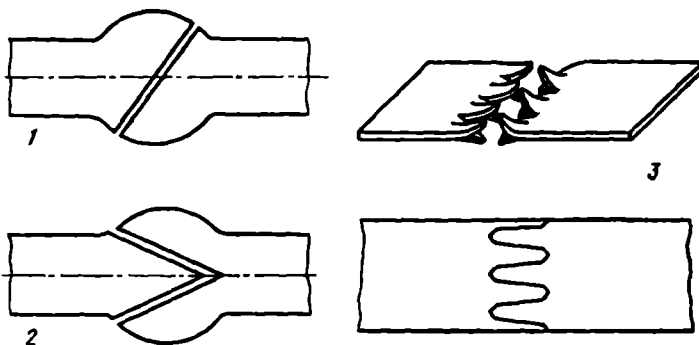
Подготовка изделий под кузнечно-горновую сварку:
